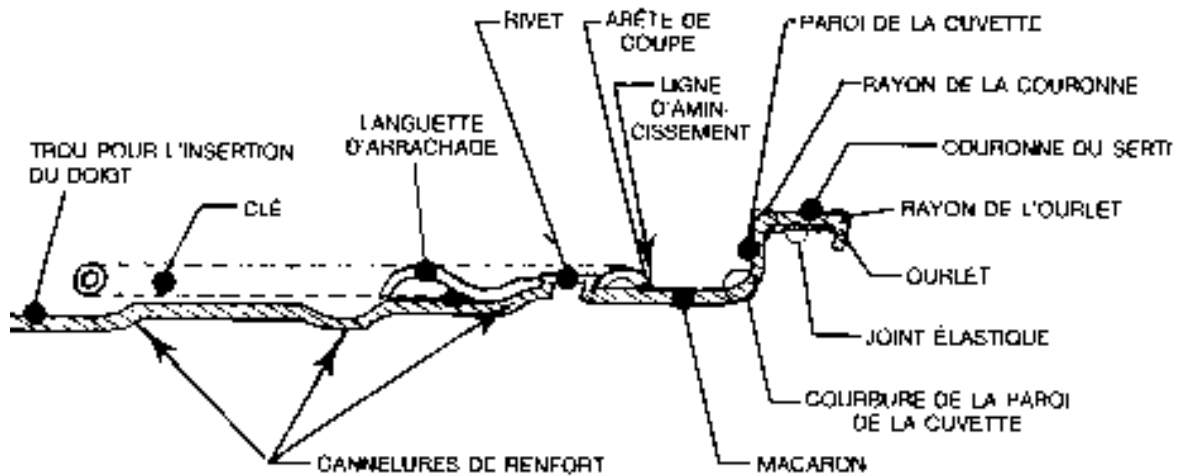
a - Fermeture de boîte à ouverture facile avec languette d'arrachage - Coupe transversale
